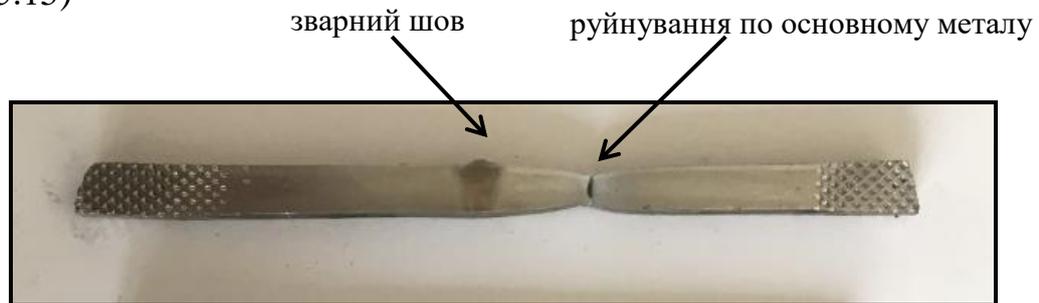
Загальний вигляд зразка сталі 10ХСНД після зварювання в середовищі захисних газів та руйнування
